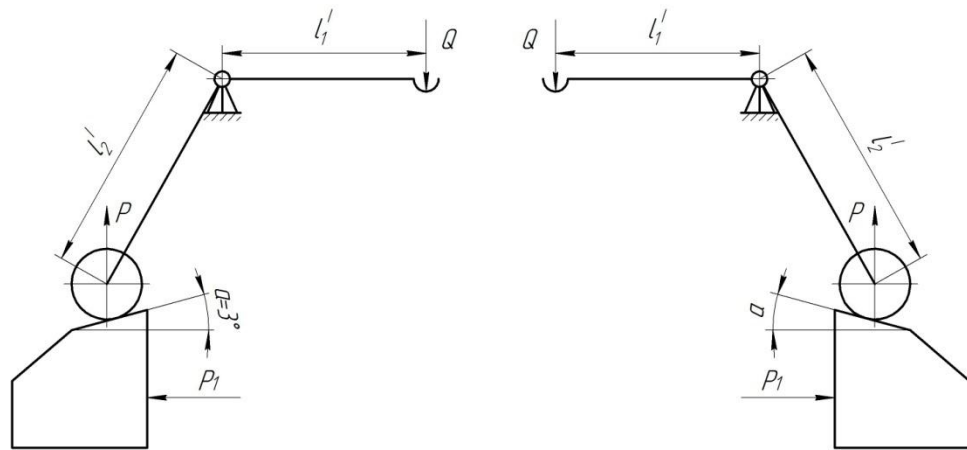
Принципова схема фрезерного пристрою.
